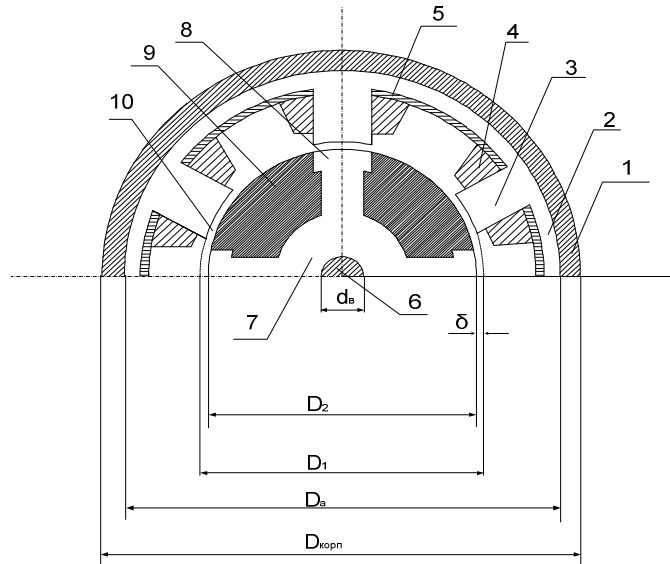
Поперечный разрез погружного вентильно-индукторного двигателя
